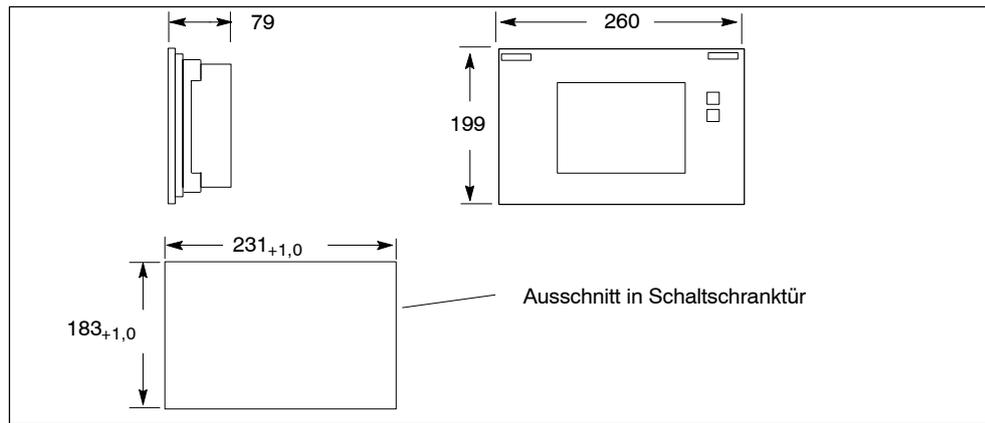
Maßbilder für das C7-635 Touch (Maße in Millimeter)
